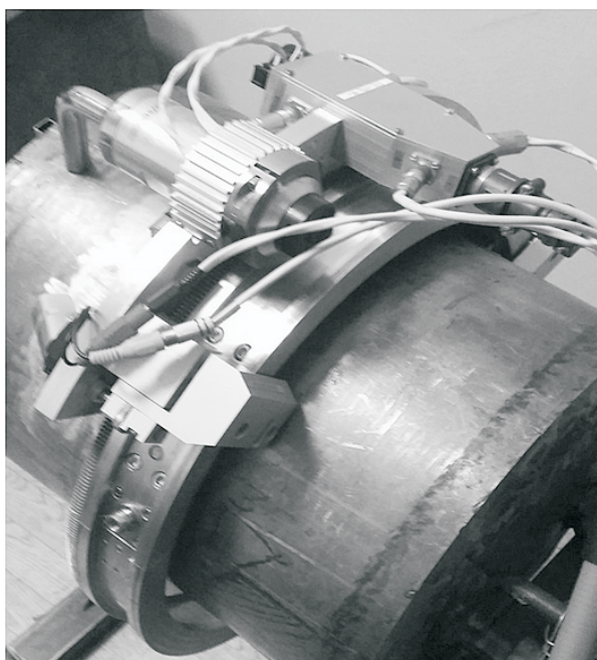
Внешний вид автоматизированного устройства ультразвуковой обработки сварных соединений в процессе сварки
